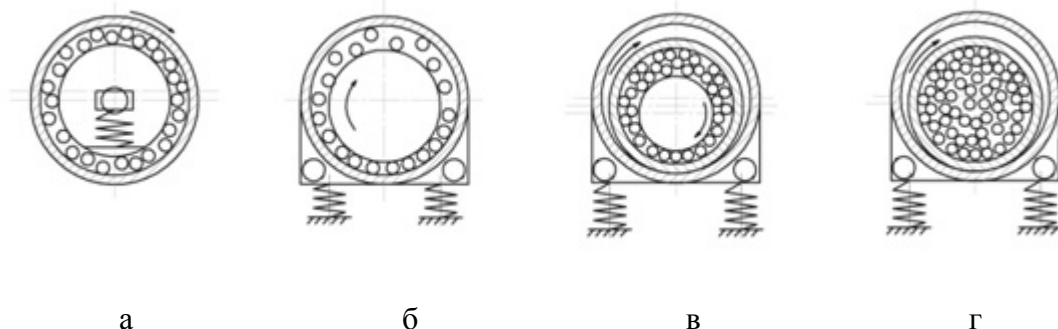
Принципові схеми вібротомашин для зміцнення внутрішніх поверхонь деталей
